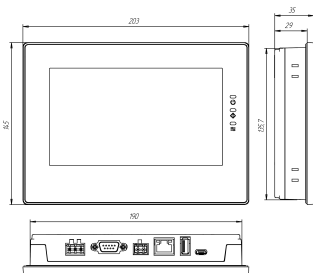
Габаритные размеры СПОТ-07.Х
